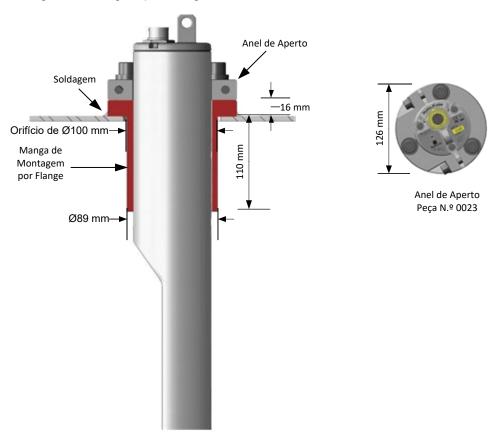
Manga de Montagem por Flange (peça n.º 0024A)
